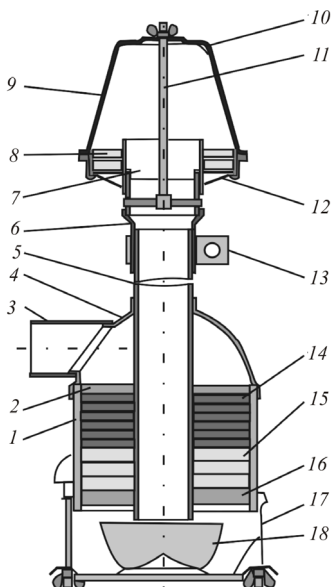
Фильтр очистки воздуха дизеля Д-243: 1 – корпус; 2 – обойма опорная; 3 – патрубок боковой; 4 – головка; 5 – центральная труба; 6 – патрубок; 7 – распределитель; 8 – завихритель; 9 – колпак; 10 – щели; 11 – шпилька; 12 – сетка; 13 – хомут; 14, 15 – фильтрующие элементы; 16 – обойма замковая; 17 – поддон; 18 – чашка
